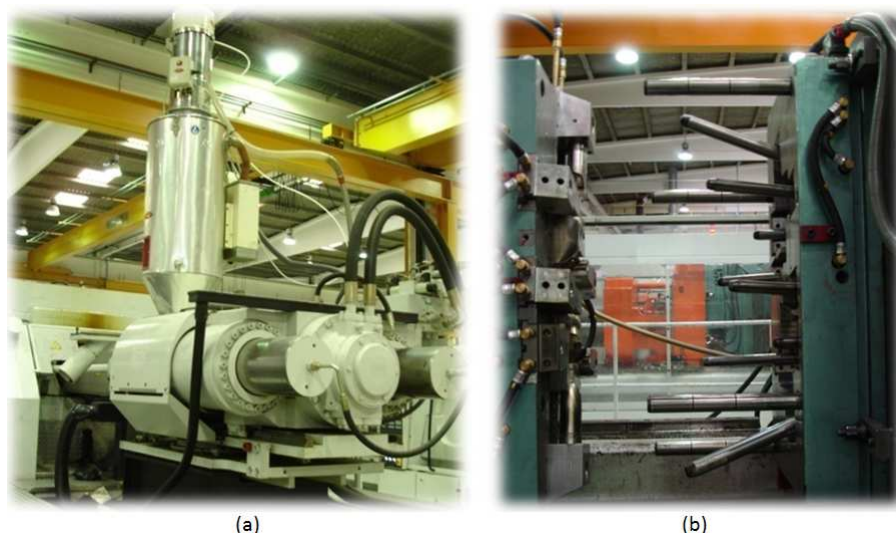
a) Máquina Injectora: ENGEL 500 Ton. (b) Molde.
